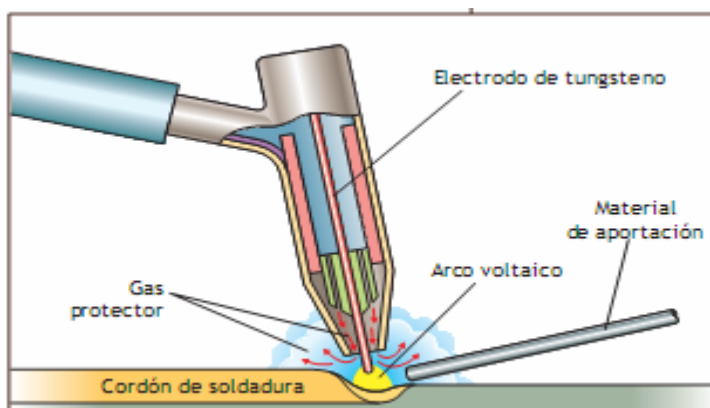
Proceso de soldadura GTAW. Fuente: Méndez y Eagar (2001).
